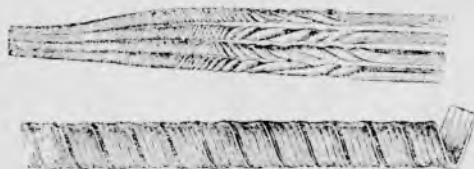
Сварка 4 полос в ленту и ленты—в трубку.
